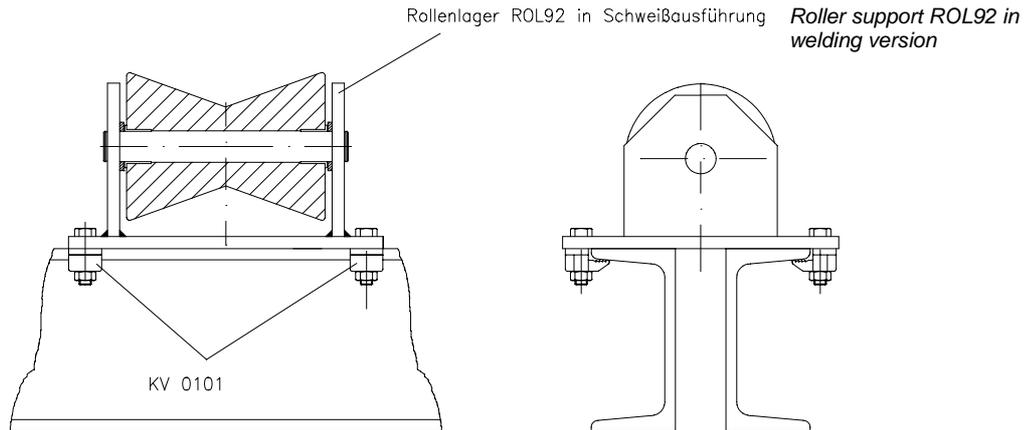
Rollenlager ROL92 in Schweißausführung zur Klemmbefestigung
